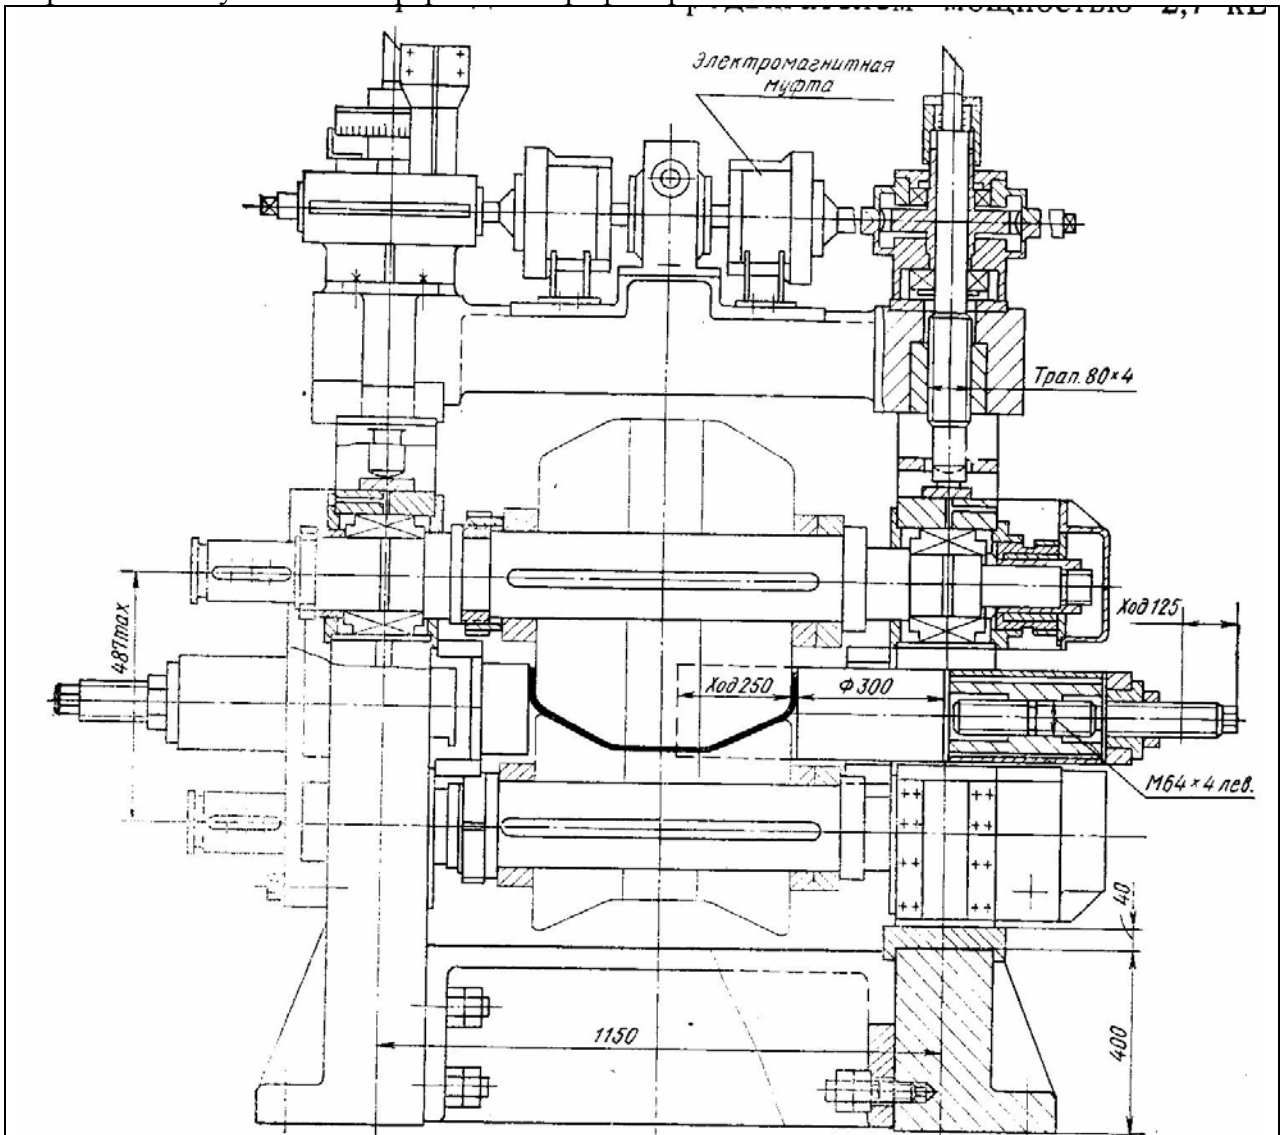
Рабочая универсальная клетка профилегибочного стана.
